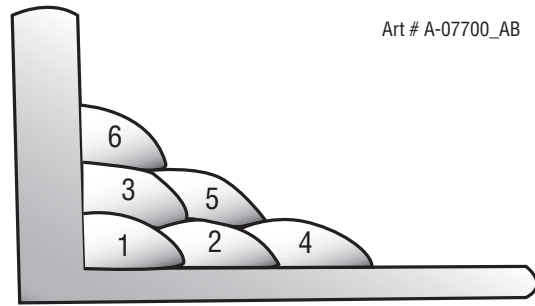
Plusieurs passages d'une soudure d'angle HV
